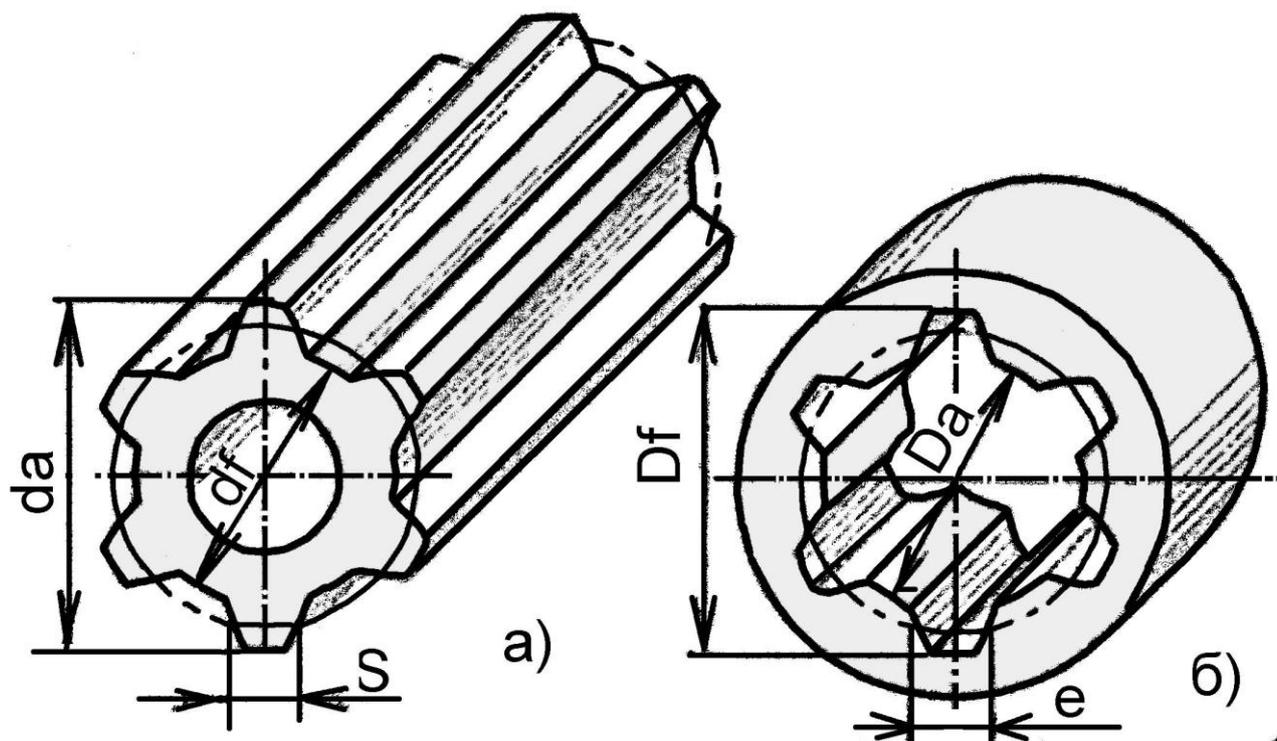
Эвольвентные шлицевые: а-вал, б-втулка
